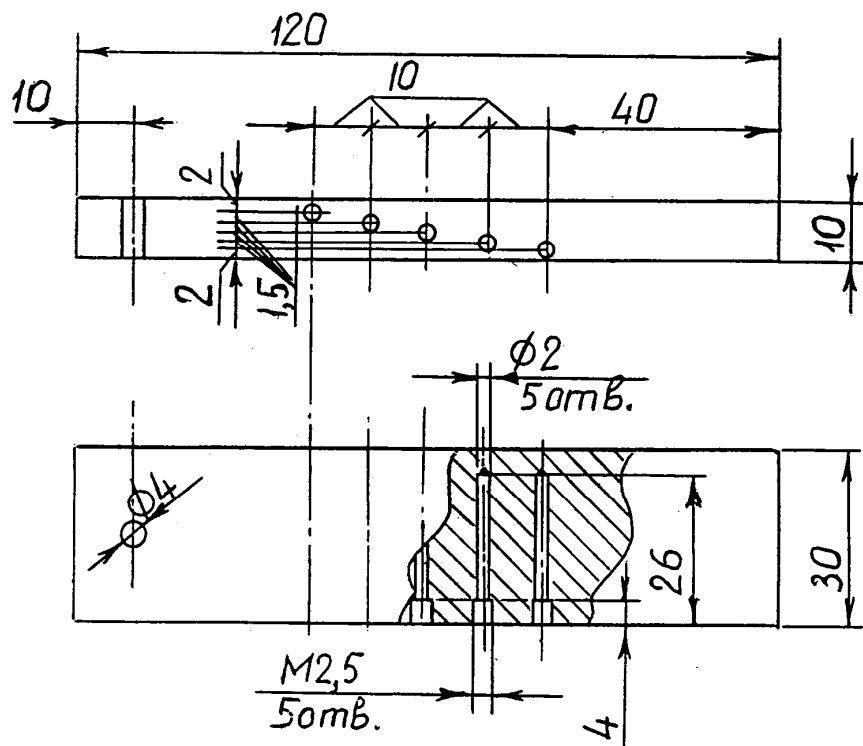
Контрольный образец МО-3 Г.С. Шелихова
